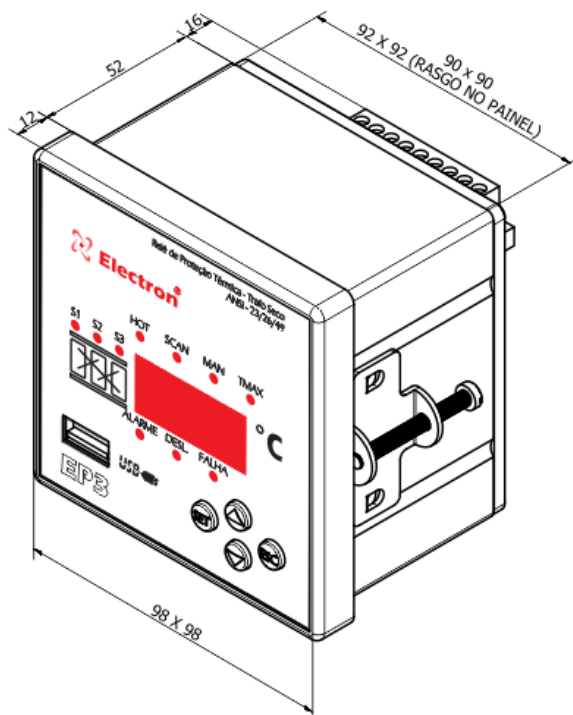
DIMENSIONS para equipamentos modelo com USB
